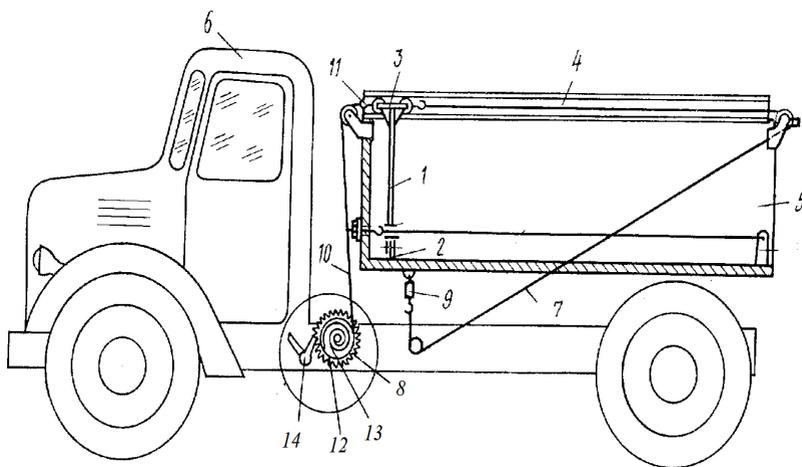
Предохранительное устройство для кузова самосвала сельскохозяйственного назначения:
